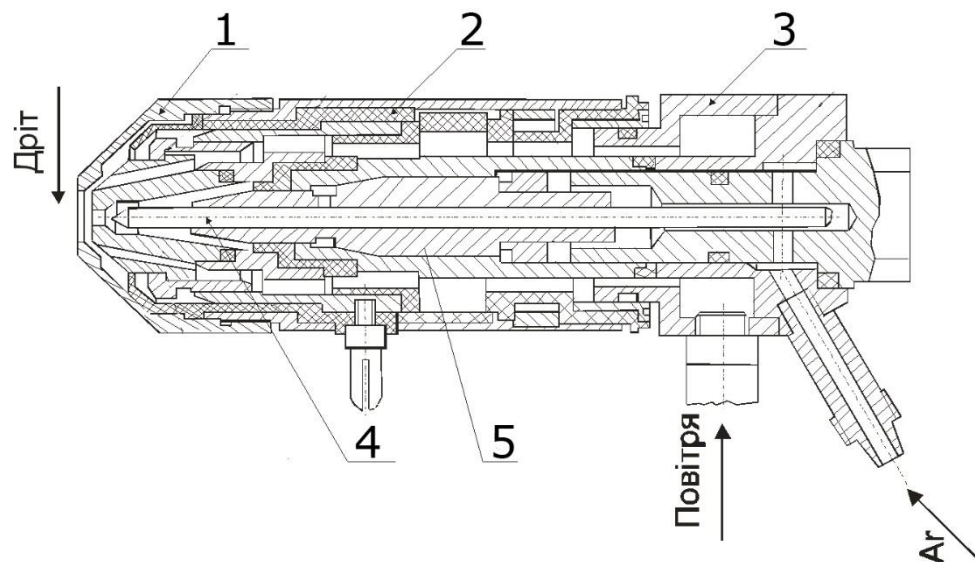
Схема плазмотрона для плазмо-дугового напилення із рухомим дротом-анодом: 1 – кришка; 2 – ізоляційний корпус; 3 – корпус; 4 – катод; 5 – затискач.
